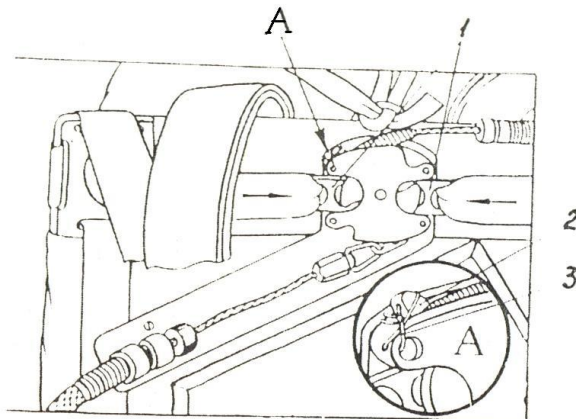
Контровка затвора двухконусного замка с корпусом:
